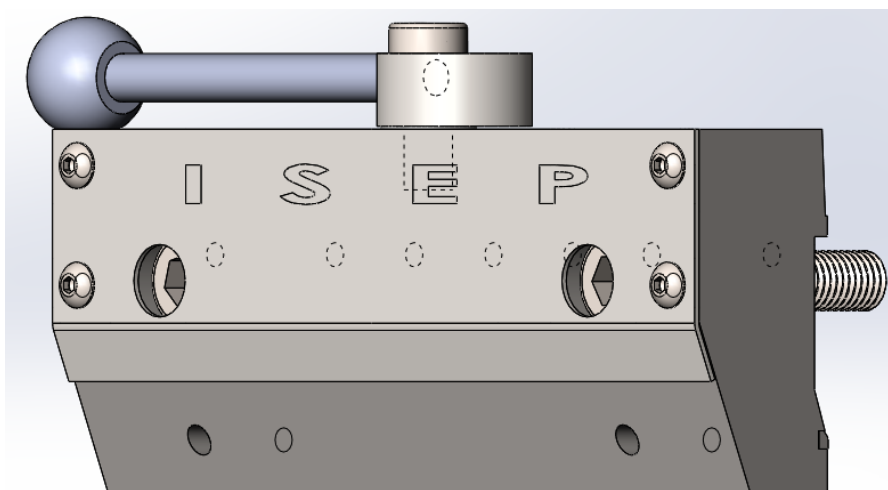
Chapa de protecção - Suporte_5 - Mola de lâmina
